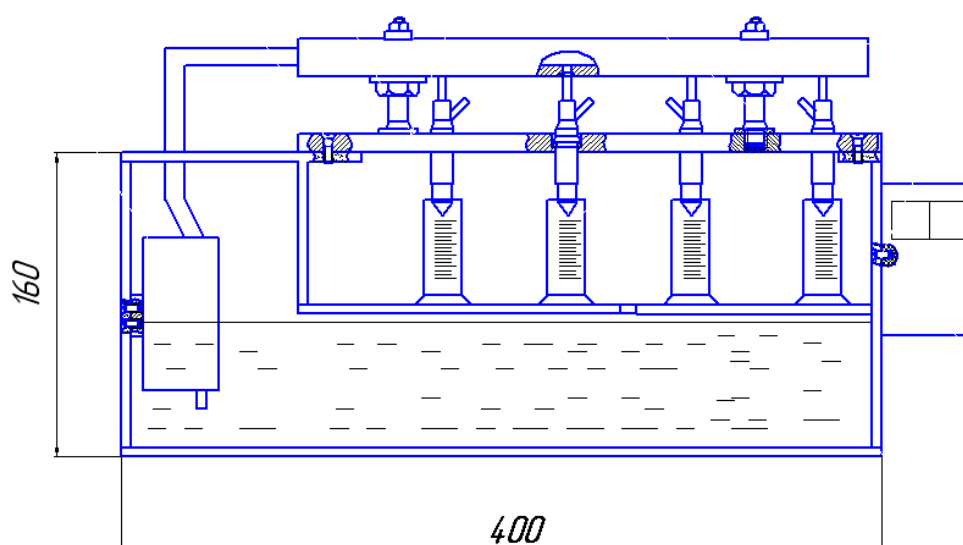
Устройство для промывки и диагностики форсунок инжекторного двигателя.
